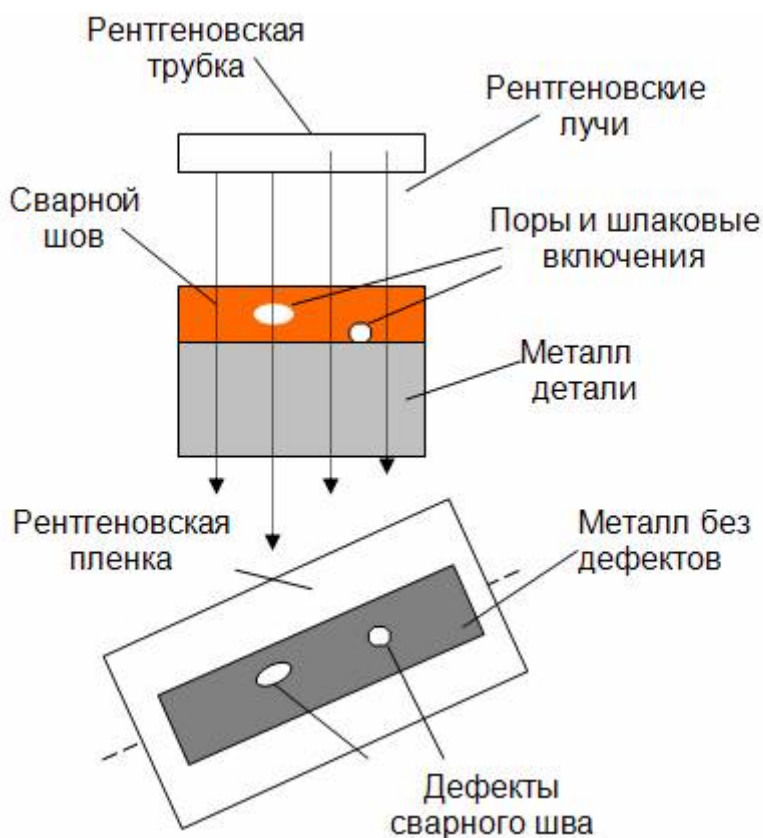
Контроль качества сварки и сварных соединений рентгеновским методом
